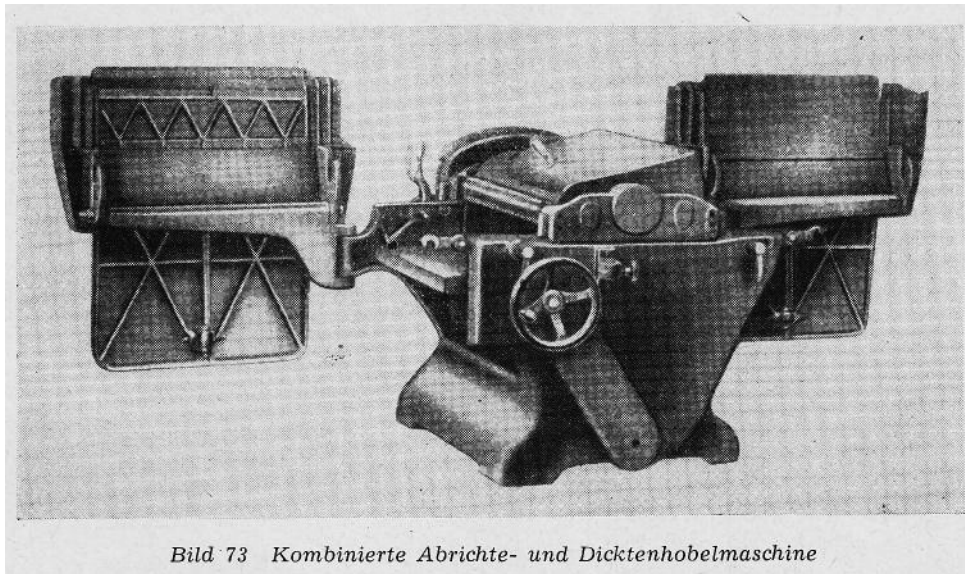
Kombinierte Abrichte- und Dicktenhobelmaschine
